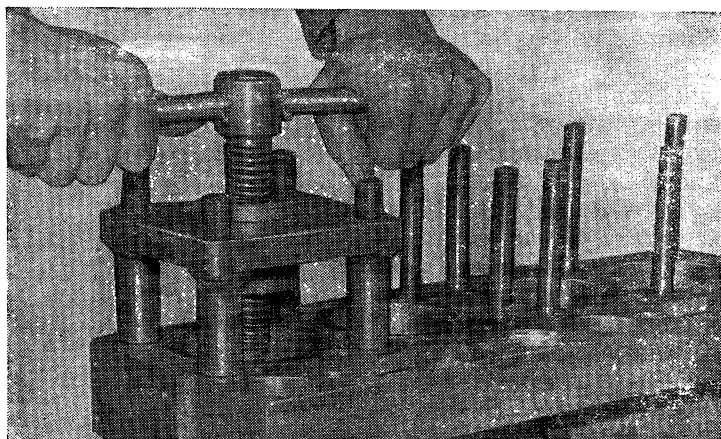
Приспособление для выпрессовки гильз цилиндров.
